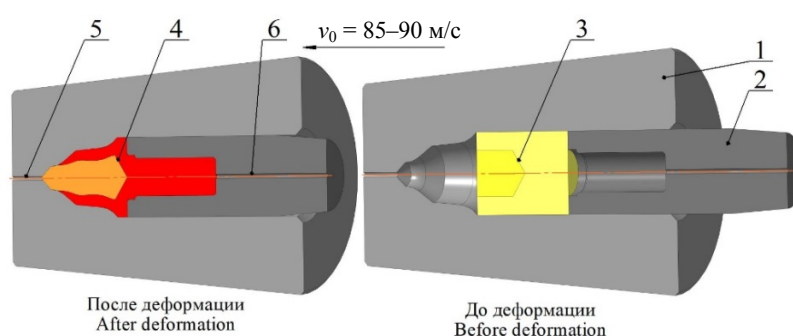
Схема деформирования для скоростного горячего выдавливания биметаллических полуфабрикатов детали «тангенциальный резец»: 1 – полуматрица; 2 – формообразующий пуансон; 3 – составная заготовка; 4 – биметаллический полуфабрикат; 5, 6 – газоотводящие каналы
